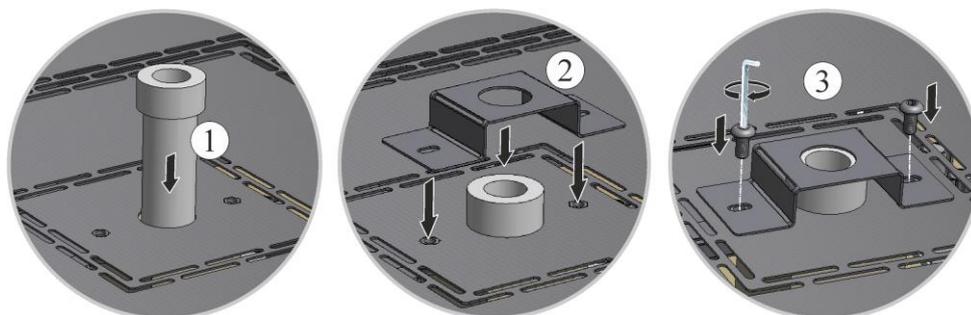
Montagem do tubo do ar de exaustão (semelhante à figura)
